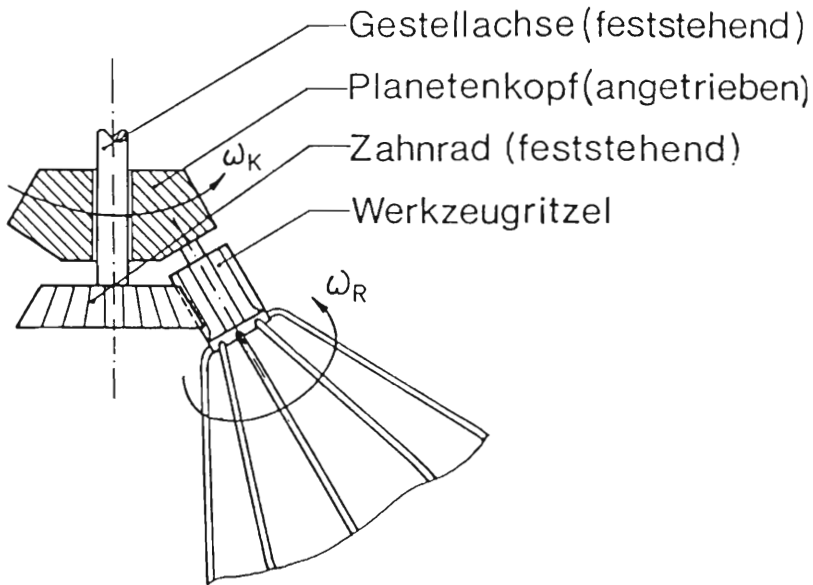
/2: Planetenkopf mit Schlagwerkzeug;
